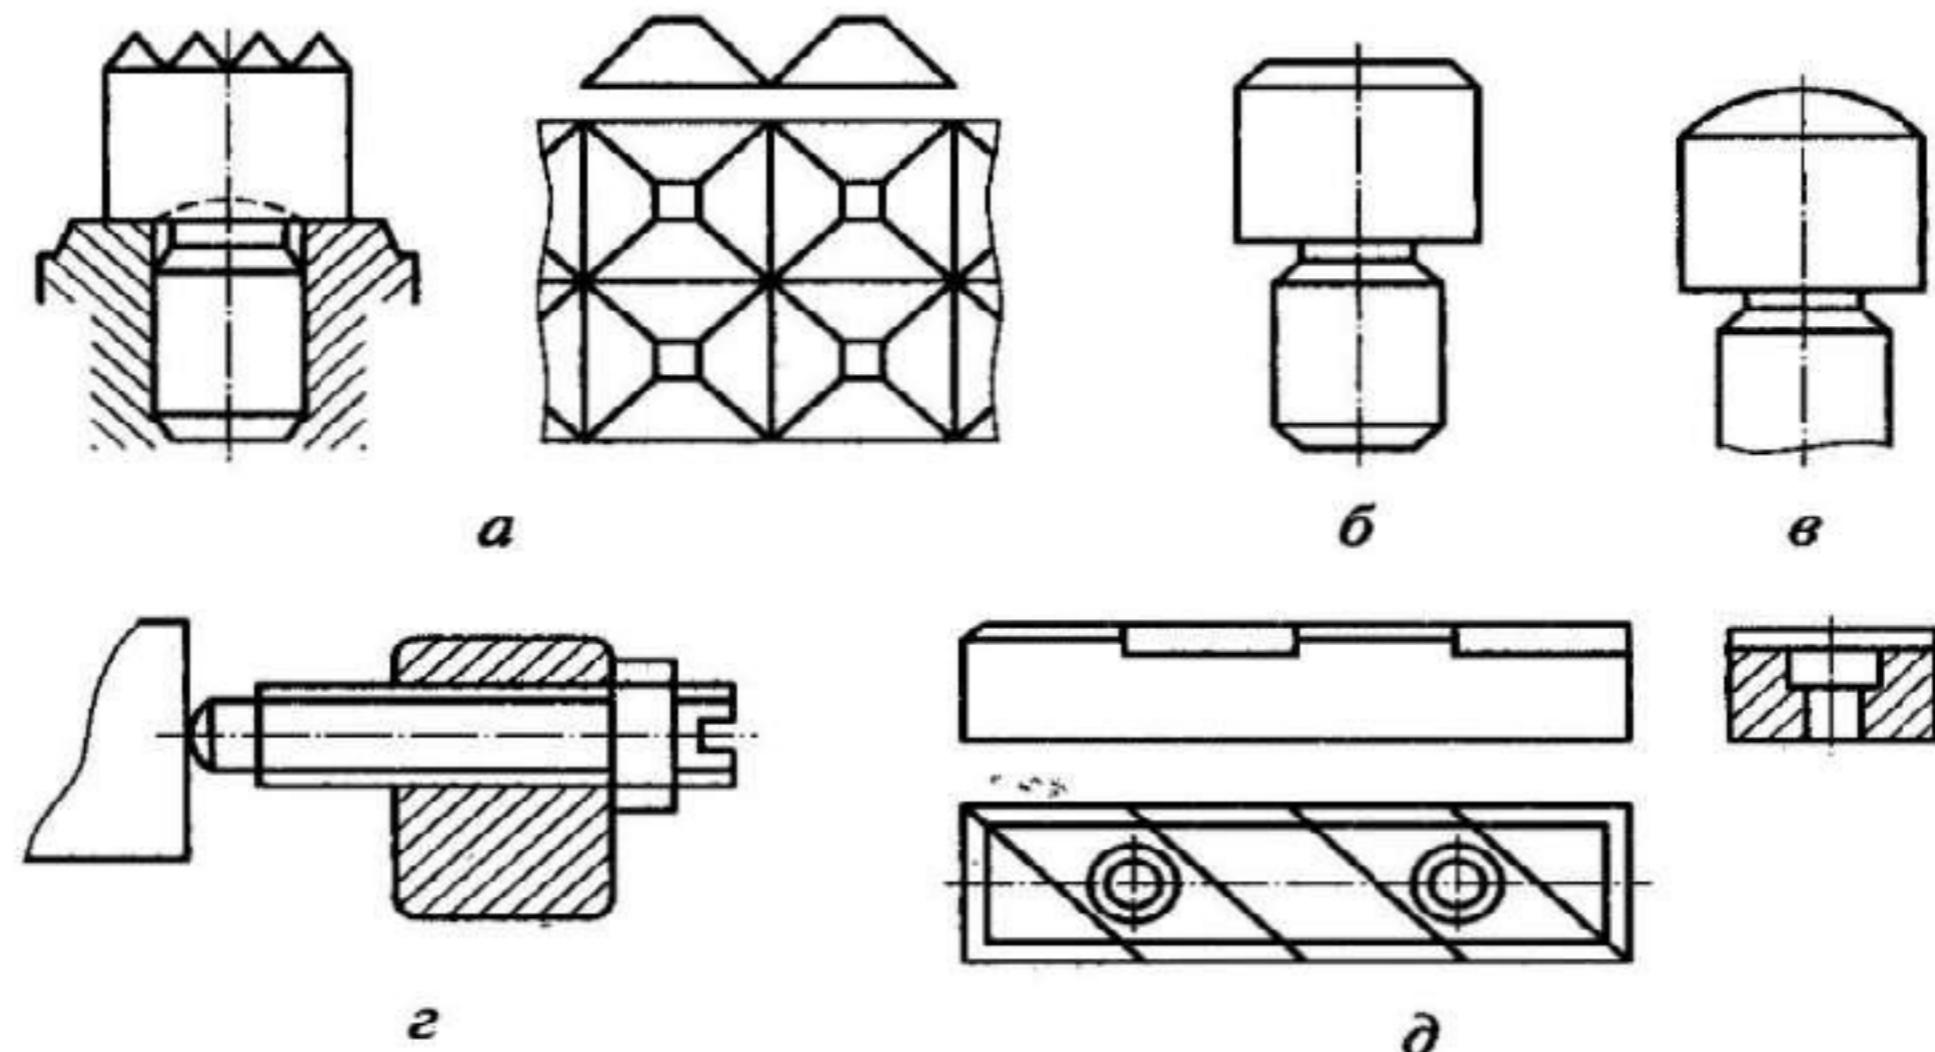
Опоры для установки деталей на плоские поверхности: *а* — с рифленой головкой; *б* — с плоской головкой; *в* — со сферической головкой; *г* — регулируемые; *д* — опорные пластины
